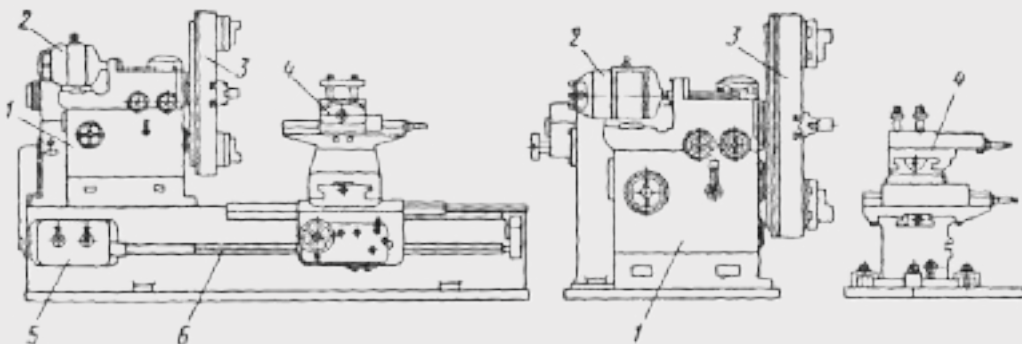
Лобові токарні верстати: 1 — передня бабка; 2 — електродвигун привода головного руху; 3 — планшайба; 4 — супорт; 5 — коробка подач; 6 — ходовий вал
